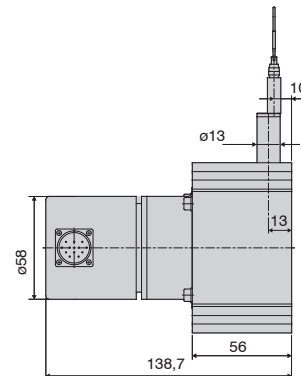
Maßzeichnung WDS- ... - P96 - BH -
